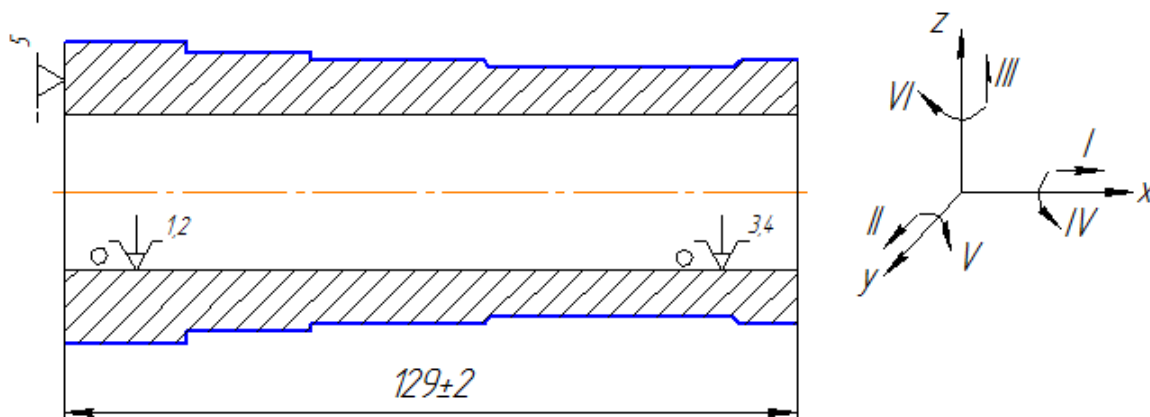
Другий спосіб базування та закріплення заготовки
